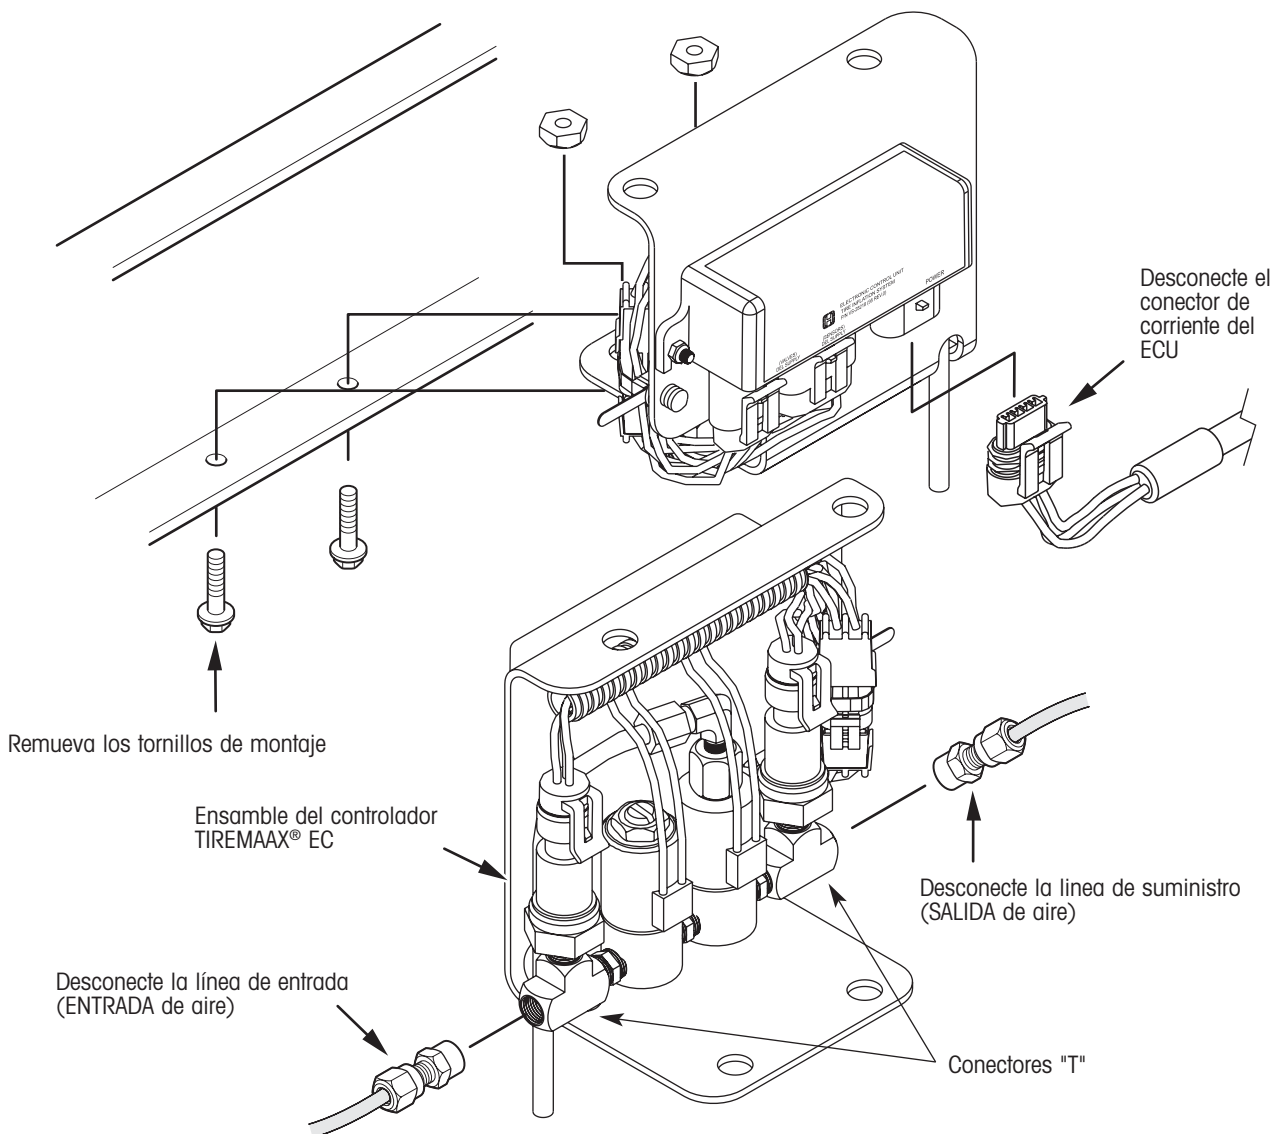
Remoción del ensamble del controlador TIREMAAX EC existente
